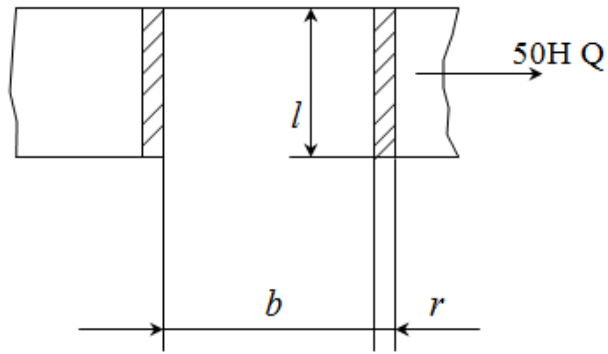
Схема для розрахунку зварного з'єднання
